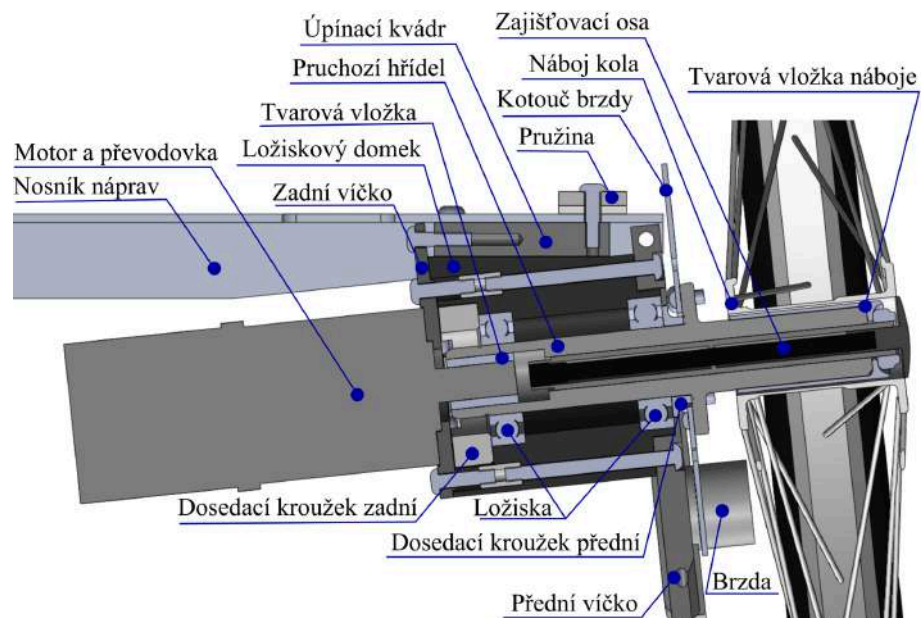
3D Model detailu příruby krokového motoru s přírubou Nema23 a planetkovými převody 15:1 a 47:1.
